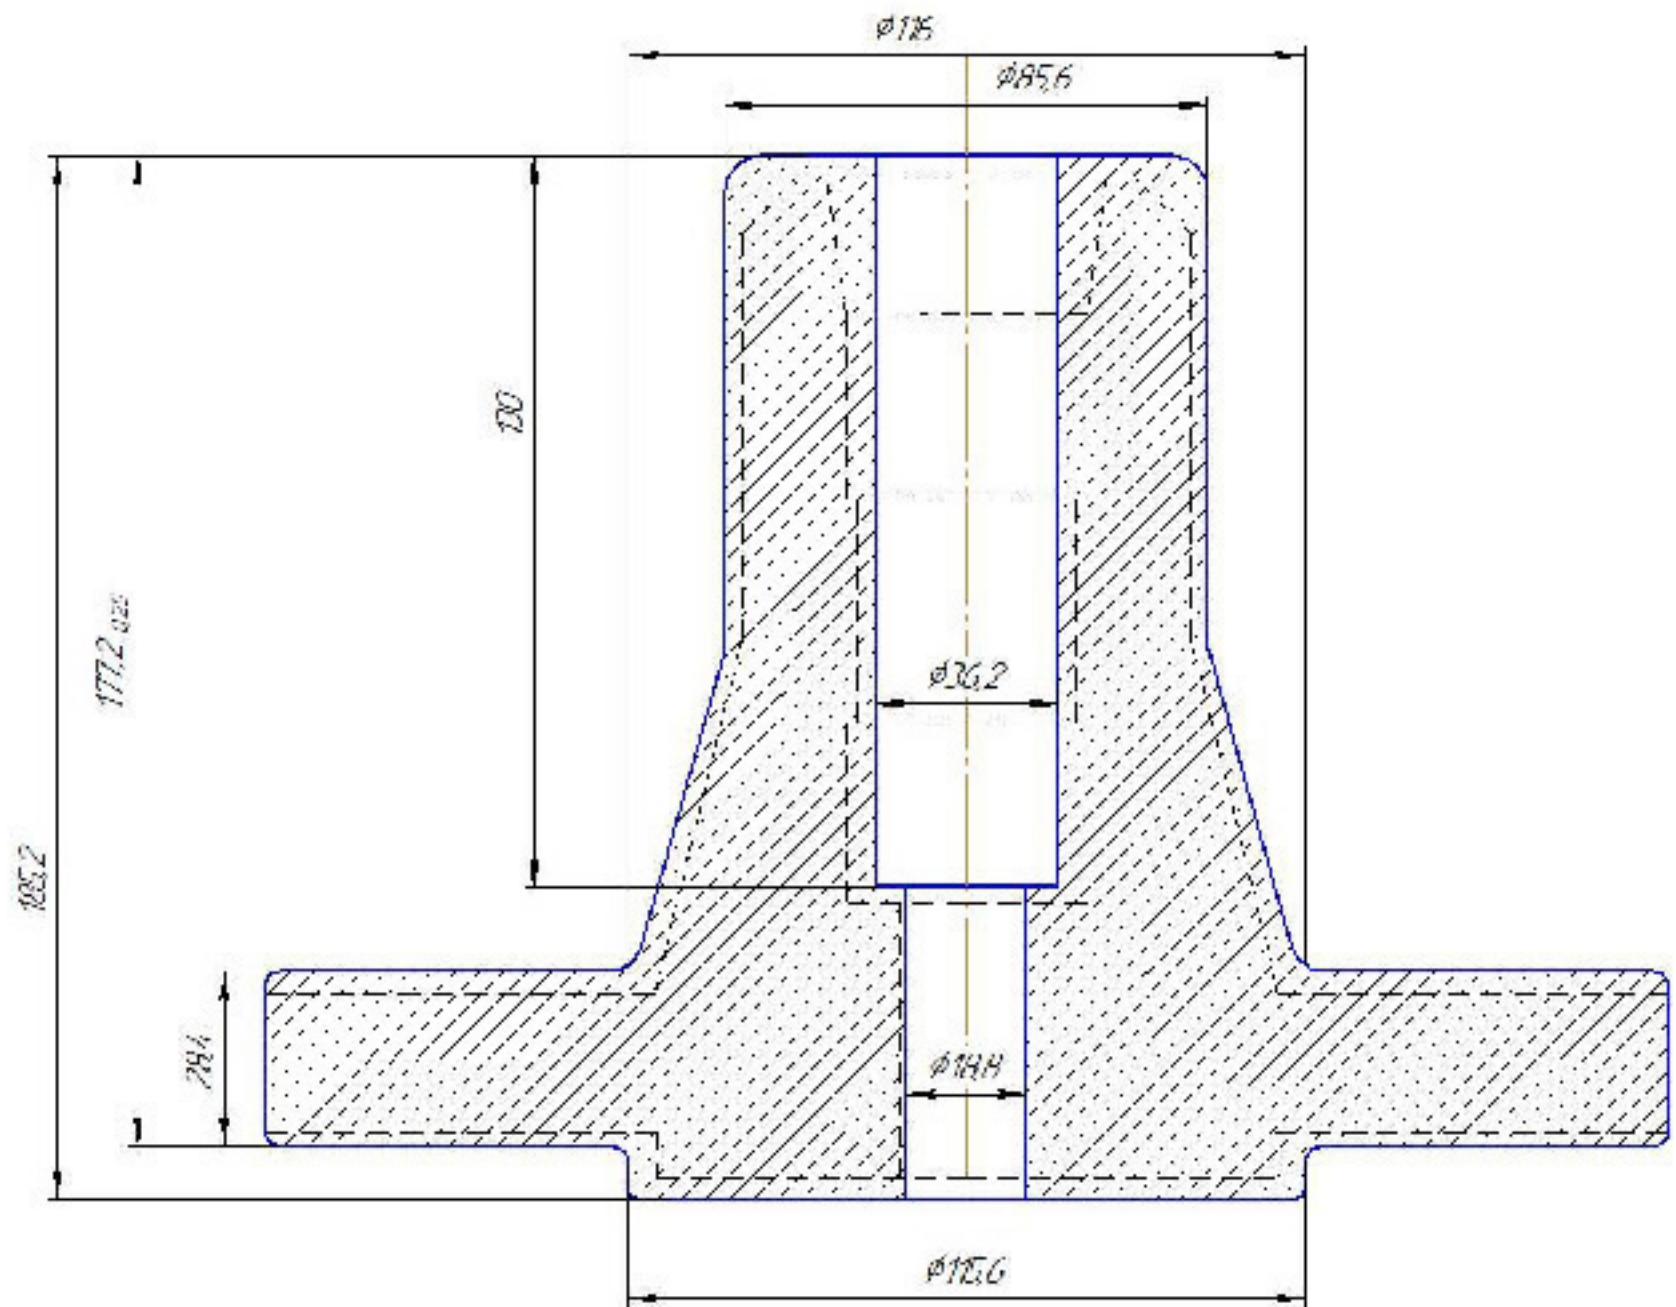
Ескіз заготовки отриманої литтям в оболонкові форми
